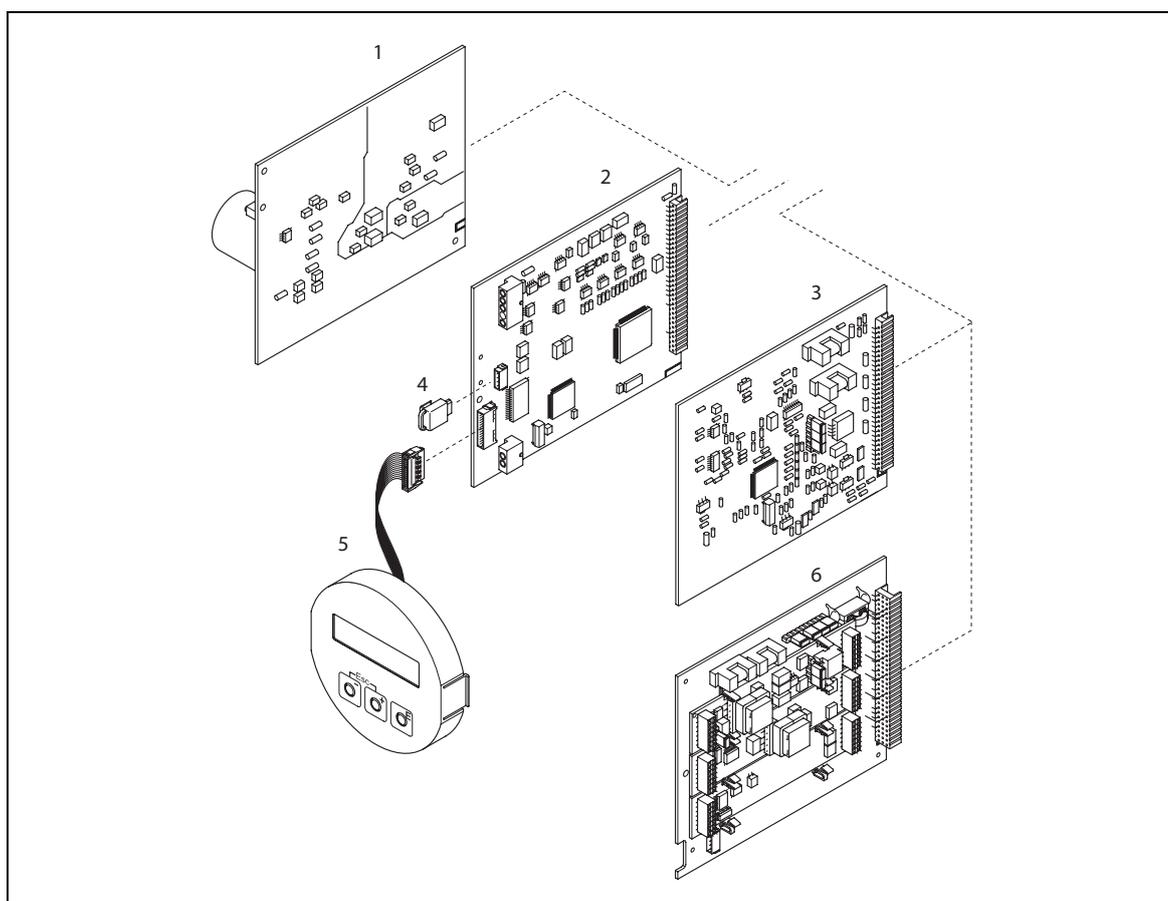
Запасные части для преобразователя Promass 80 (полевой и настенный корпуса)
